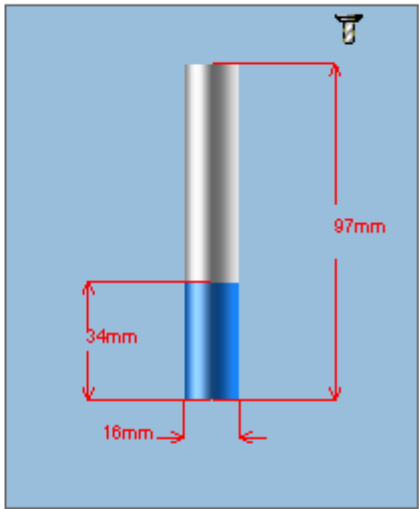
Кінцева Фреза 2P342-1600-PB P2BM
